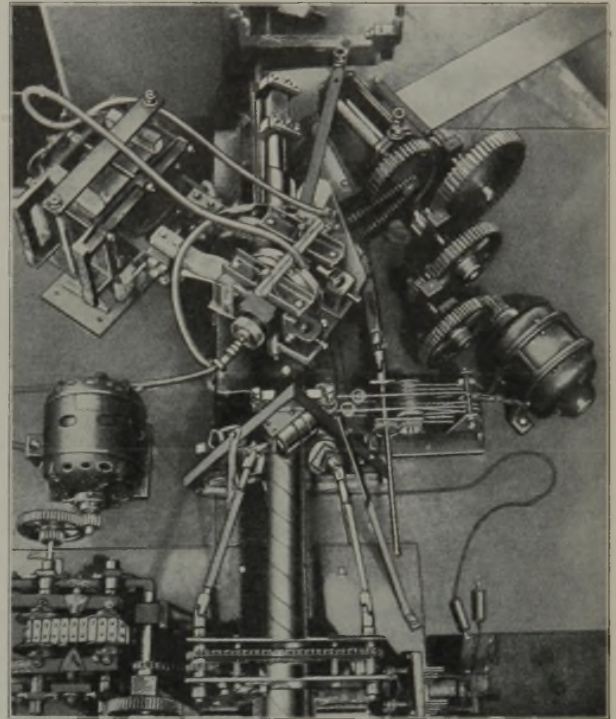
Maschine zur Herstellung von Rhren mit schraubenfrmig gewundenen Schweinhten.
